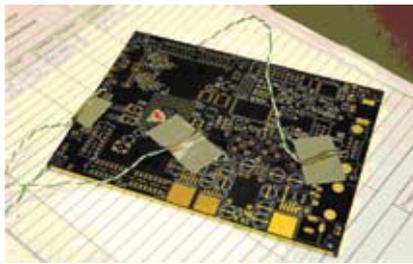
Подготовка к определению профиля пайки печатной платы перед этапом сборки
